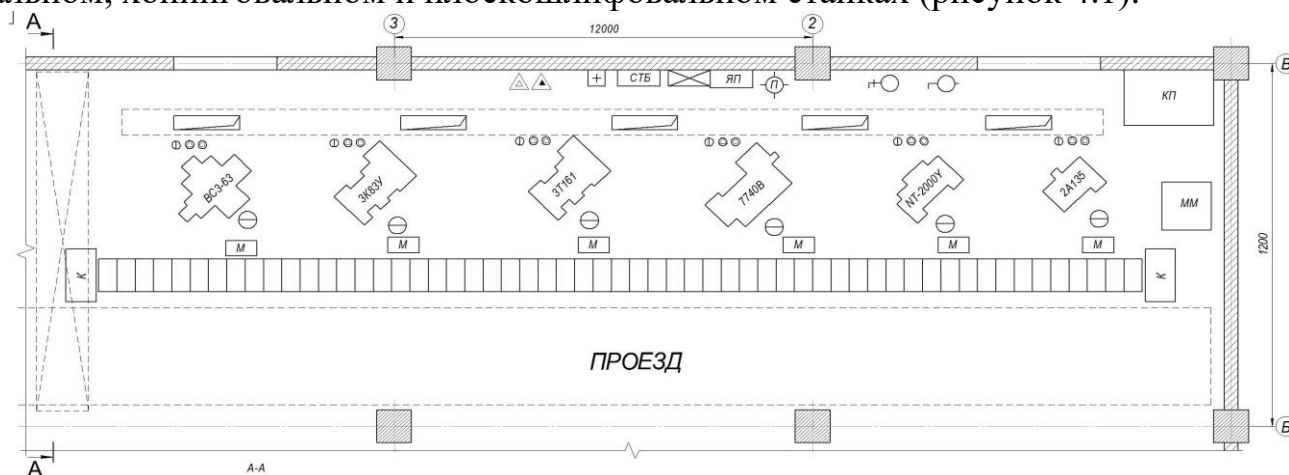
Планировка участка по изготовлению детали «Вилка полуоси»
